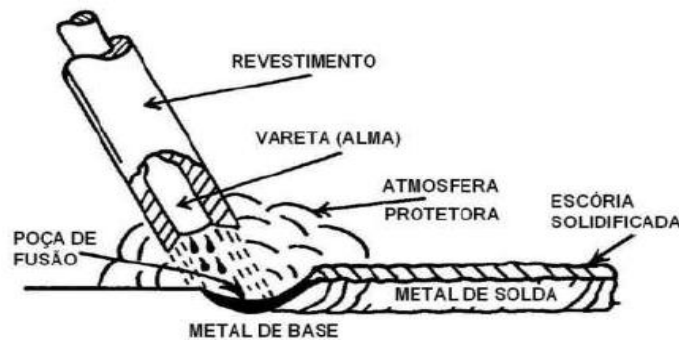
Desenho esquemático do eletrodo revestido durante uma solda. (Fonte Curso de Especialização em Soldagem, UFMG, 2015)
